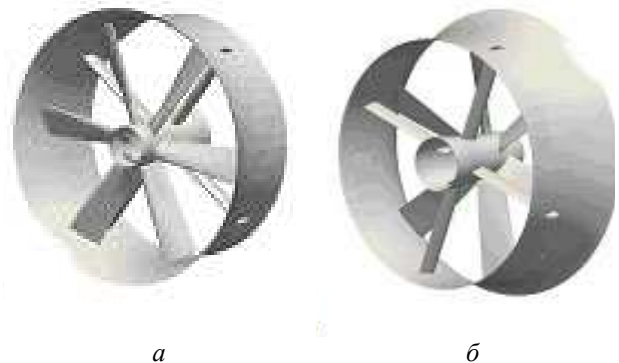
3D-модель розрахункової ділянки проточної частини ГКР ($k = 6$):
